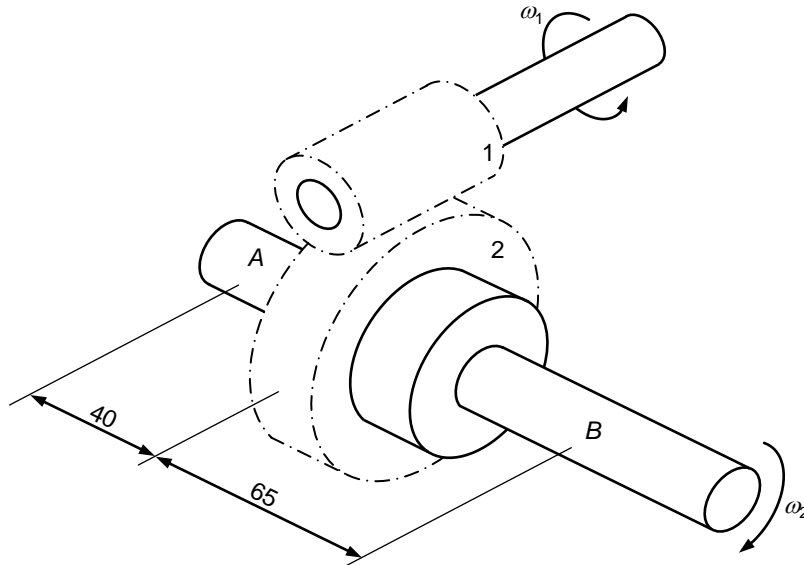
Engrenagem de parafuso sem-fim roda helicoidal.
